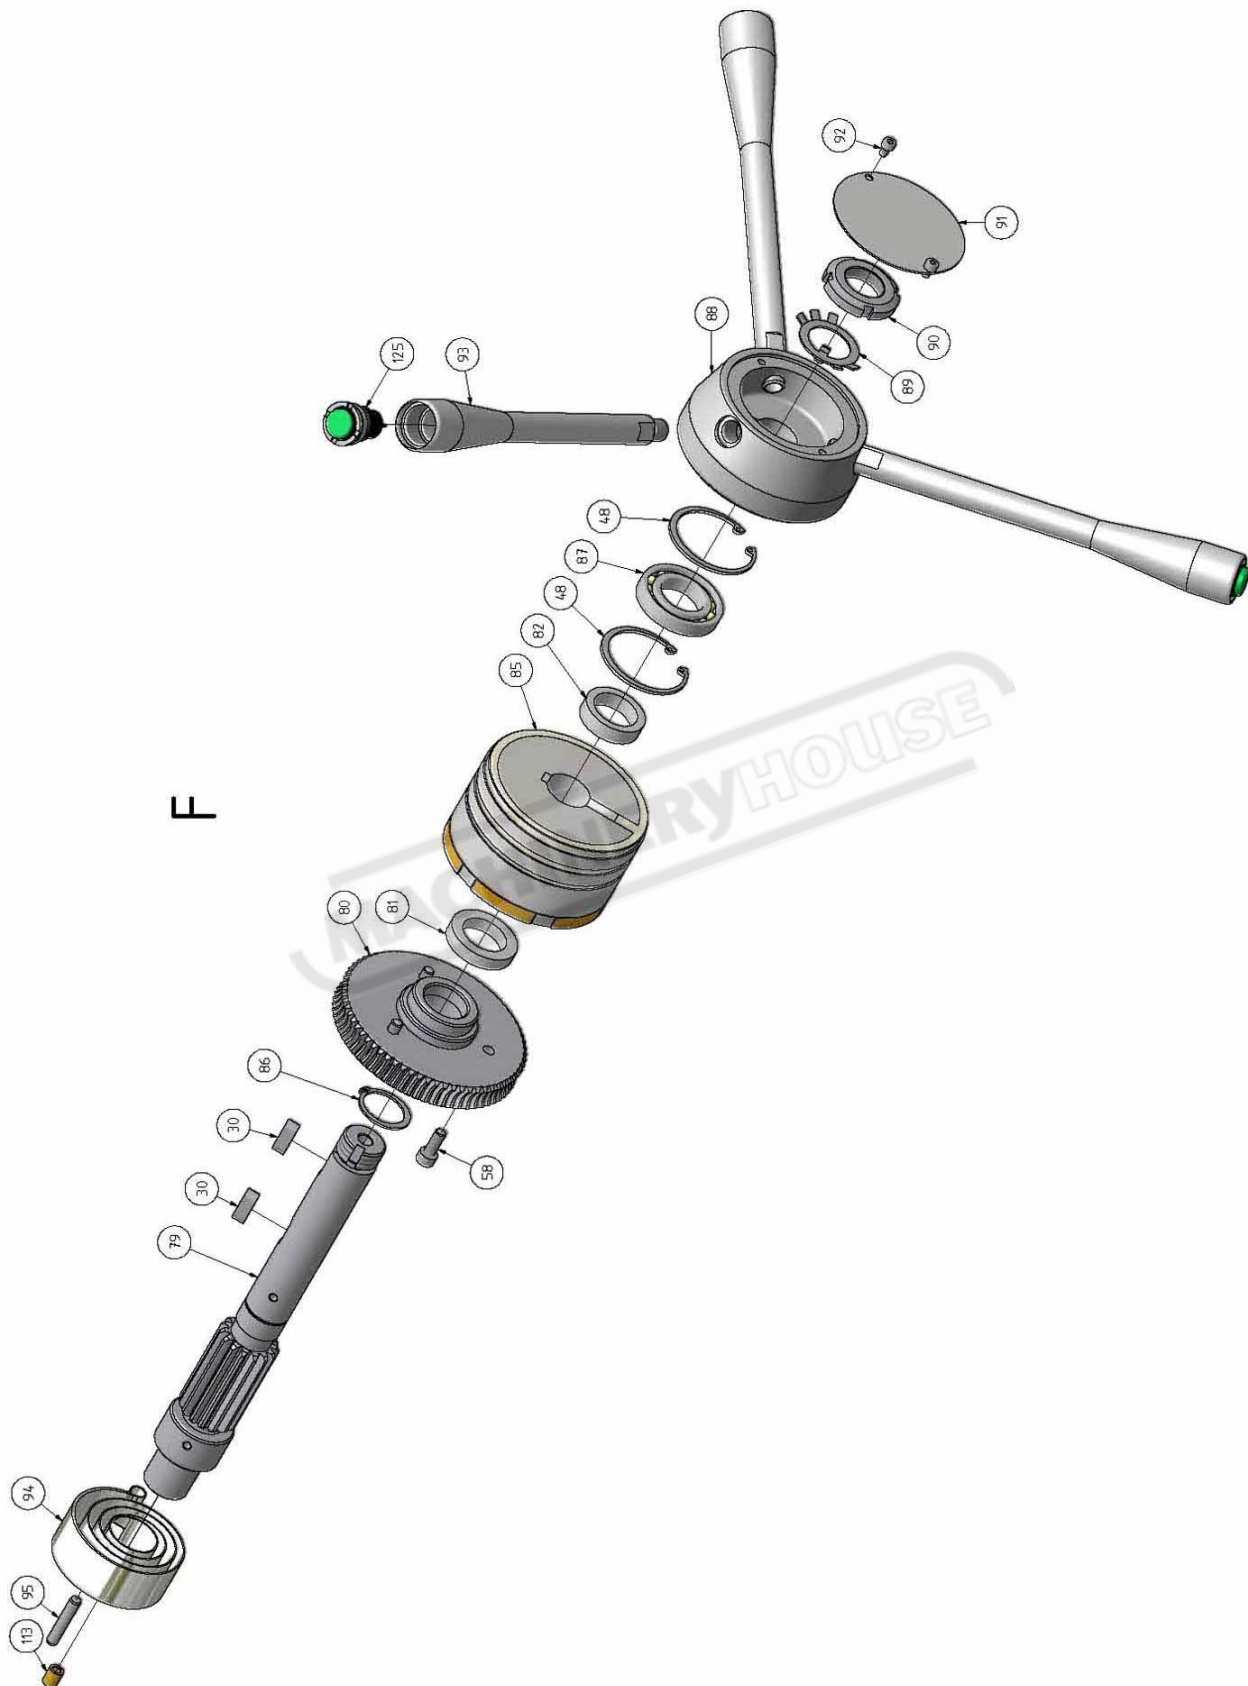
Bohrkopf 6 von 9 - Drilling head 6 of 9
